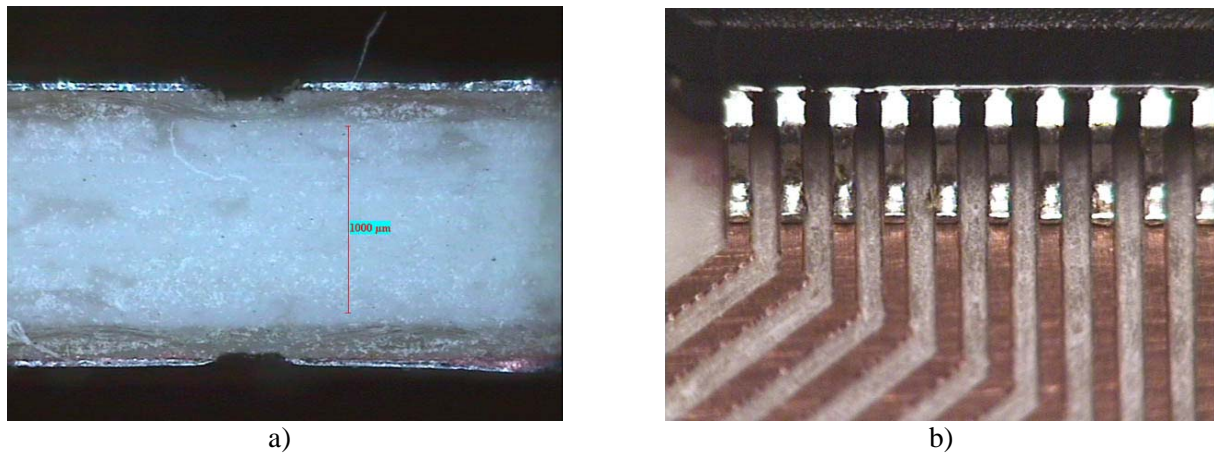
Destalle de sección transversal de un pcb y alineación de pines en encapsulado de paso fino
